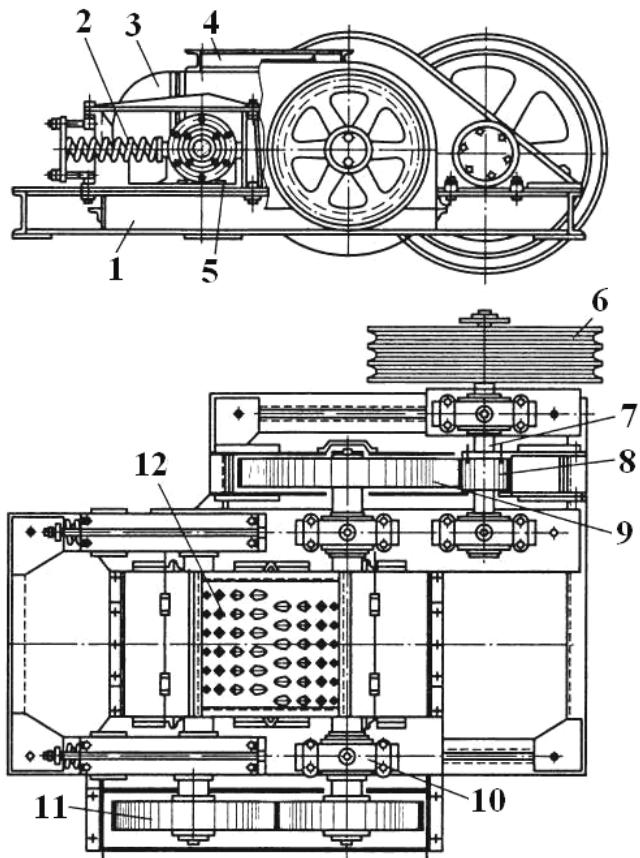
Дробилка двухвалковая зубчатая ДДЗ
